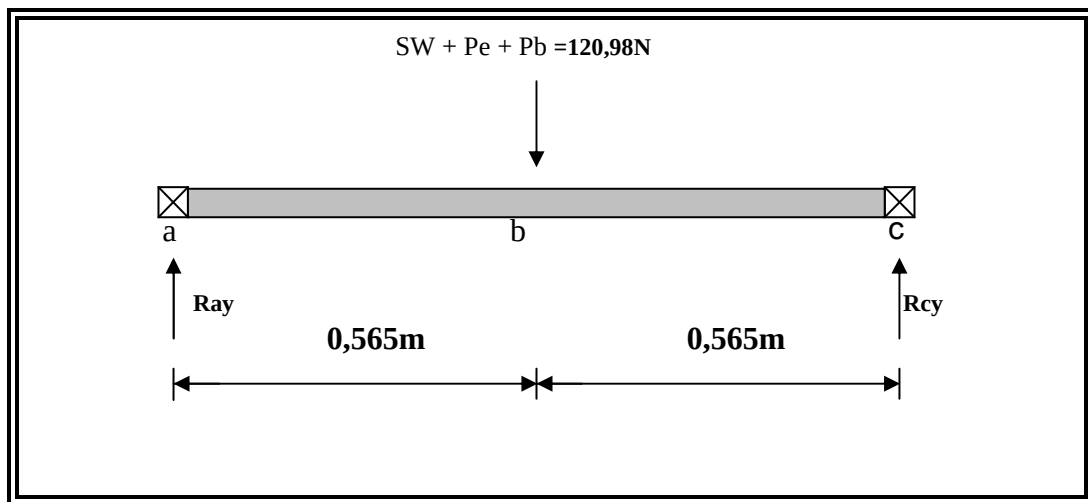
Fuerzas aplicadas sobre el eje en el plano “YZ” del transportador N° 2. Fuente:
